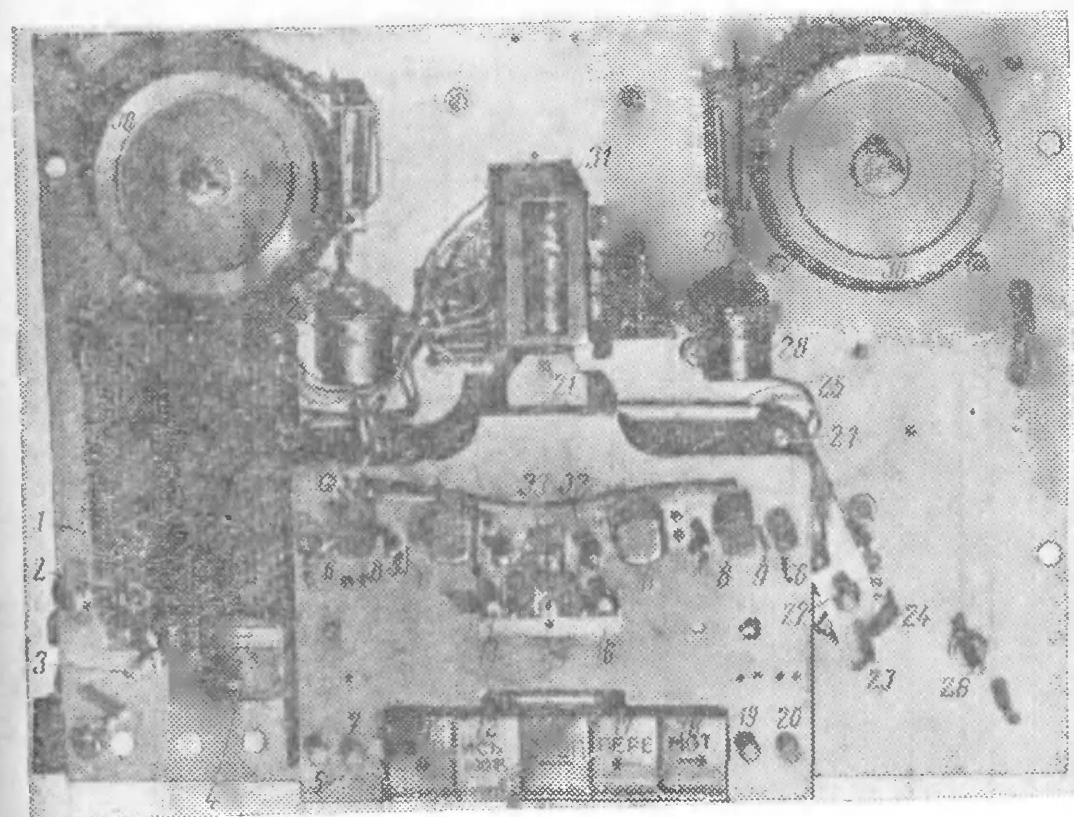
Размещение деталей на плате лентопротяжного механизма магнитофона-диктофона (вид сверху)
